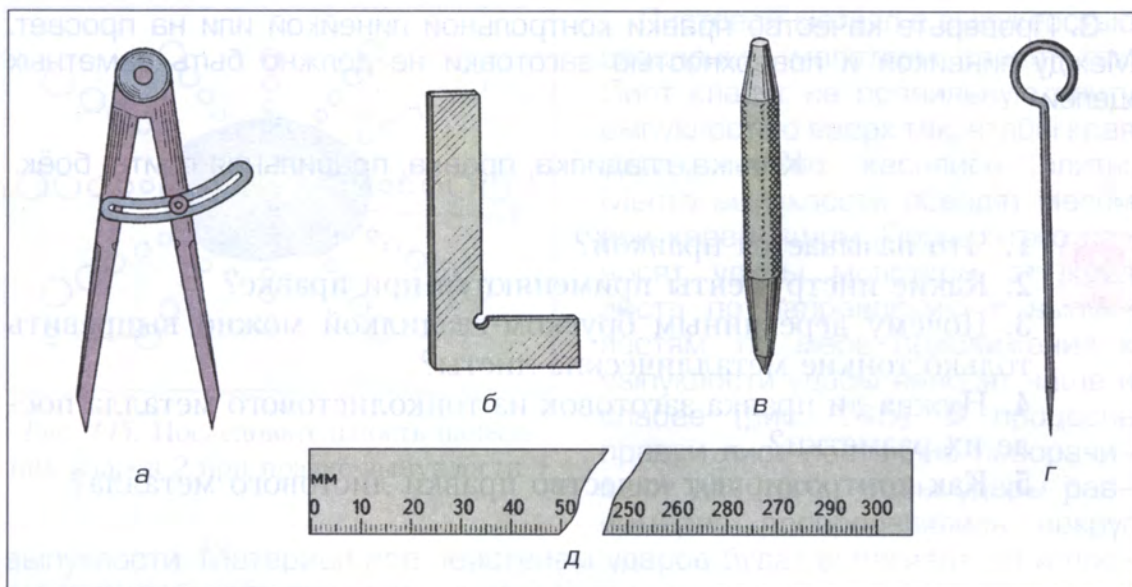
Инструменты для разметки заготовок из тонколистового металла: а – циркуль, б – угольник, в – кернер, г – чертилка, д – линейка
